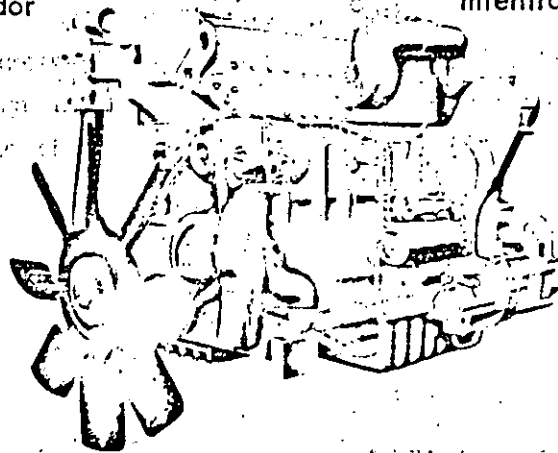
Motor Caterpillar de Diesel D343 (988)
